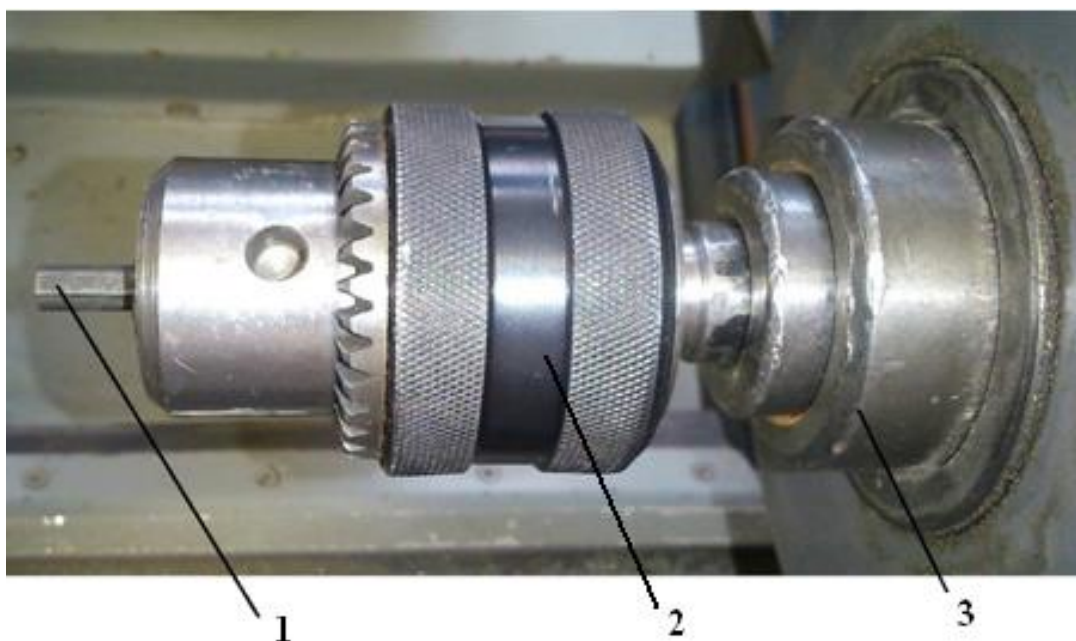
Закрепление заготовки - 1 - заготовка; 2 – патрон, 3- оснастка;
